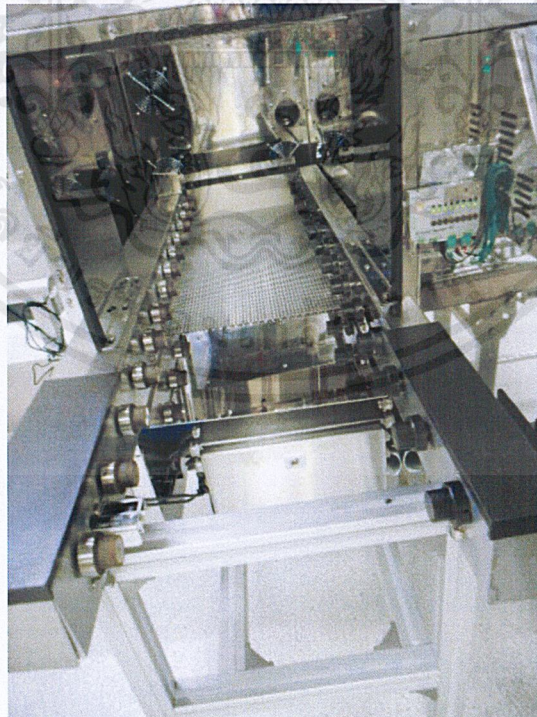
แสดง Drawing ของ Input Conveyor
